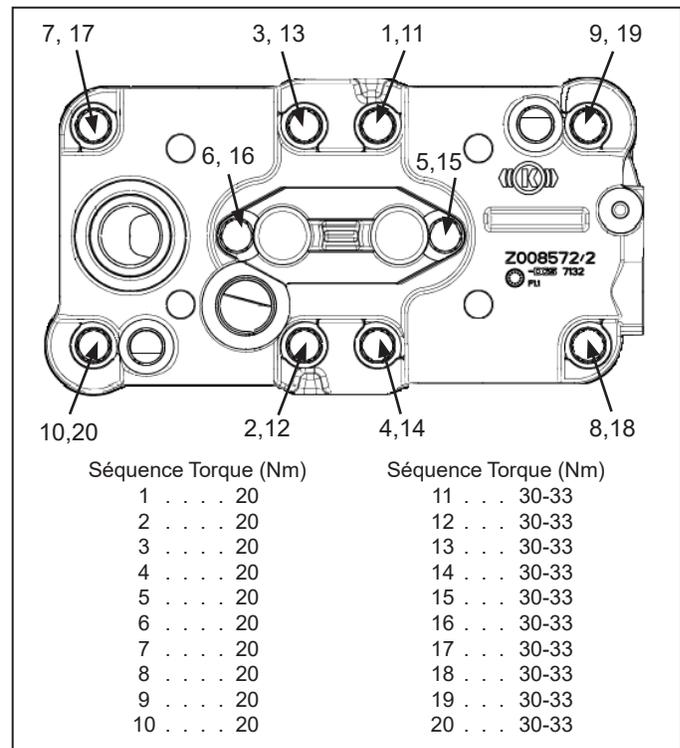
Séquence de serrage des boulons de culasse pour compresseur Bendix® 720cc
